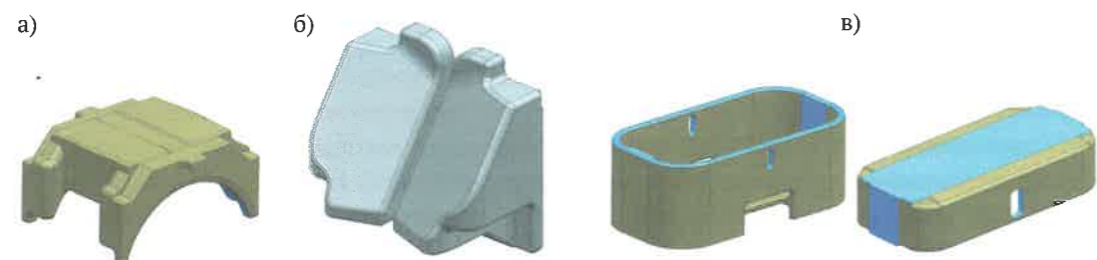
Локализованные детали из высокопрочного чугуна, где: а) адаптер; б) фрикционные клинья; в) корпус и колпак бокового скользуна
